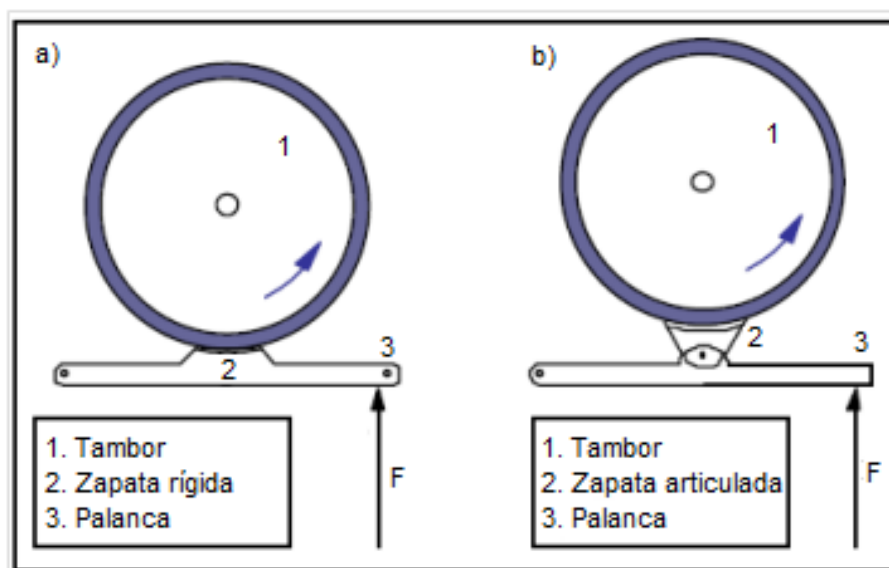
a) Freno de contracción externa zapata rígida, b) Freno de contracción externa zapata articulada <sup>10</sup>
